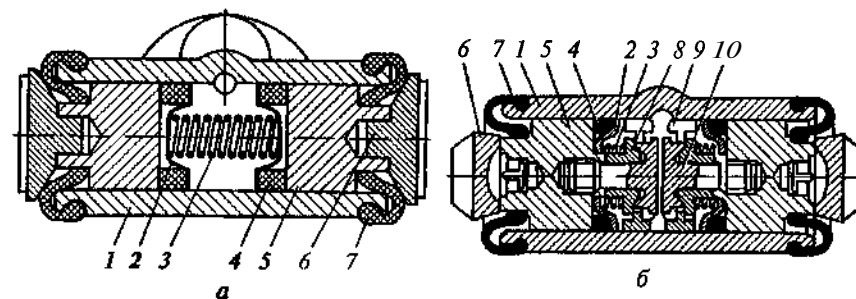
Задние колесные тормозные цилиндры легковых автомобилей ВАЗ: *a* — повышенной проходимости; *б* — переднеприводных; 1 — корпус; 2 — чашка; 3 — пружина; 4 — манжета; 5 — поршень; 6 — упор; 7 — чехол; 8 — сухарь; 9 — кольцо; 10 — винт
